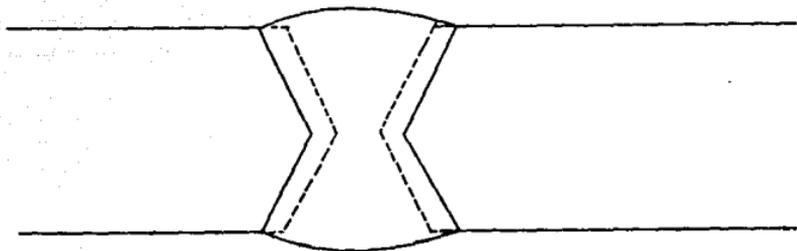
Soldadura con Bisel Doble en V
